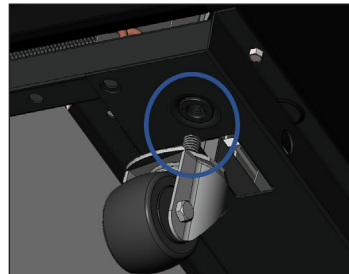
Die Befestigungsschrauben der Rollen lösen.
